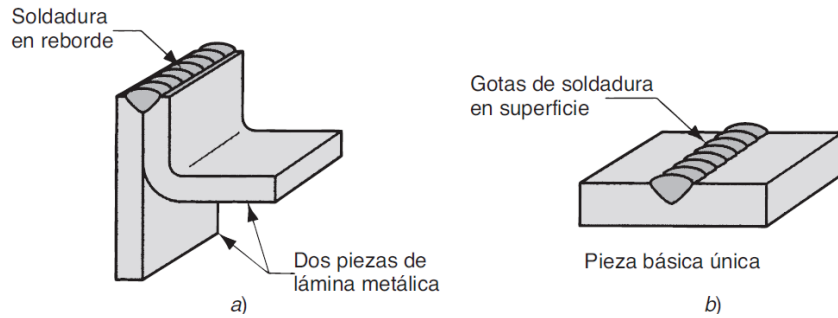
a) Soldadura en reborde y (b) Soldadura en superficie.
